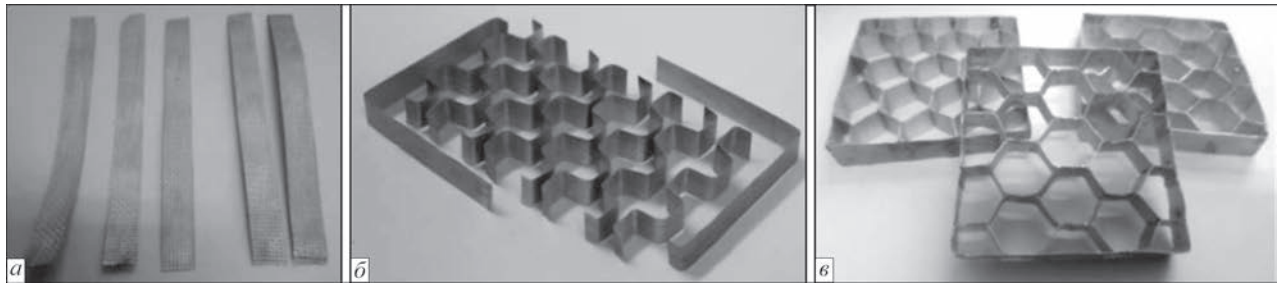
Етапи виготовлення стільникового заповнювача: а – стрічки з біметалевого матеріалу Al–Ti; б – заготовки профільованих стрічок для точкового зварювання стільникового заповнювача; в – стільниковий заповнювач розміром 72×72 мм
